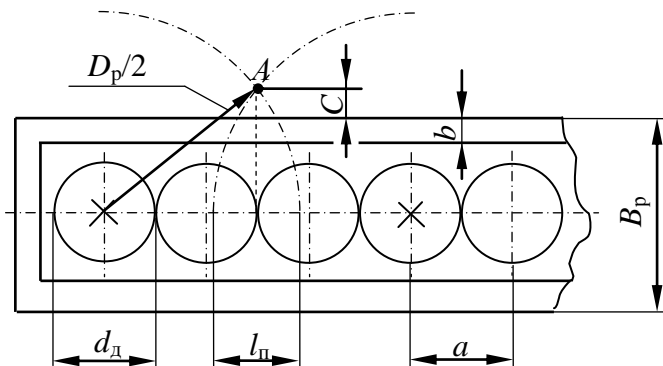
Схема к расчету необходимой величины перекрытия.
